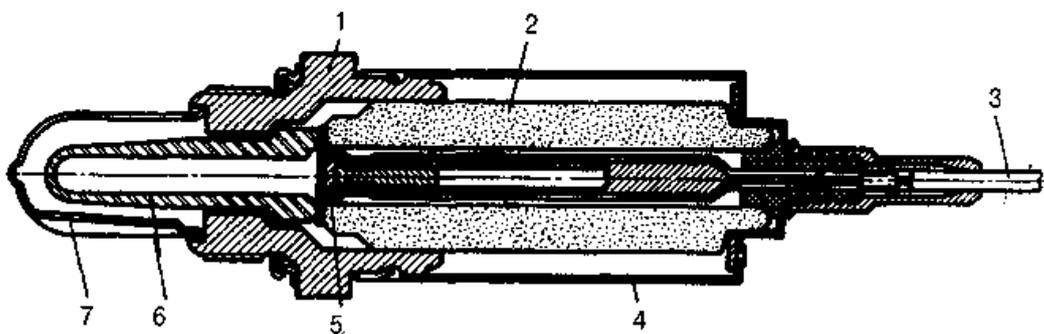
Циркониевый датчик кислорода: 1 - металлический корпус; 2 - уплотнение; 3 - соединительный кабель; 4 - кожух; 5 - контактный стержень; 6 - активный элемент из двуоксида циркония; 7 - защитный колпачок с прорезями
